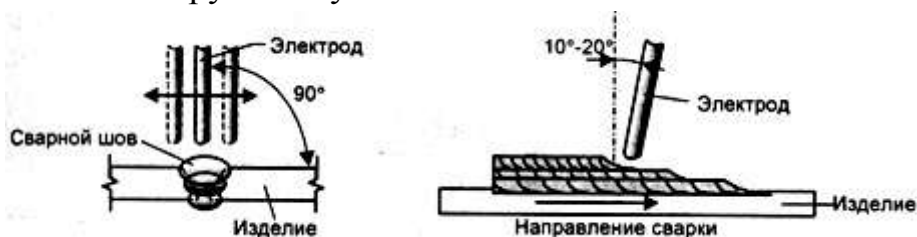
Положение электрода при сварке стыкового соединения со скосом кромок в нижнем положении.
